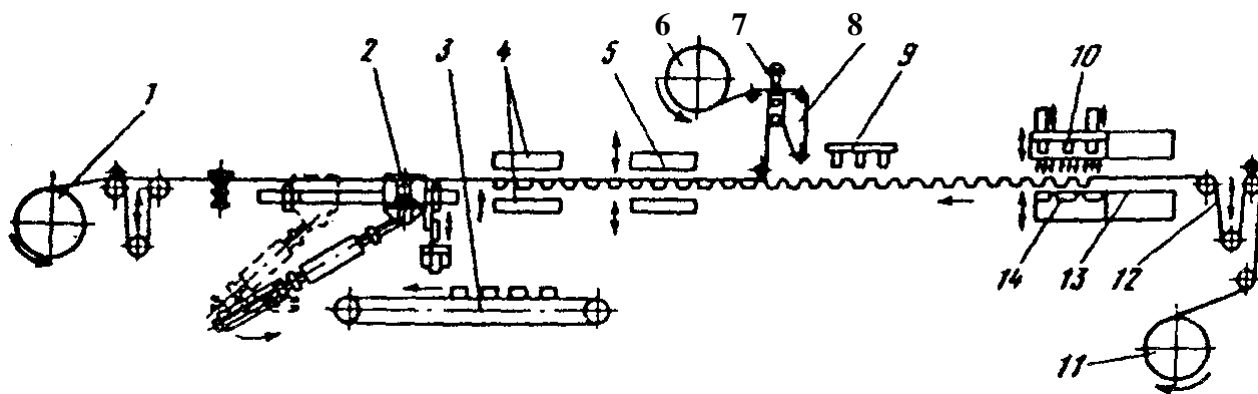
Схема роботи фасовочно-упаковочного автомата М6-ОРК-1:
